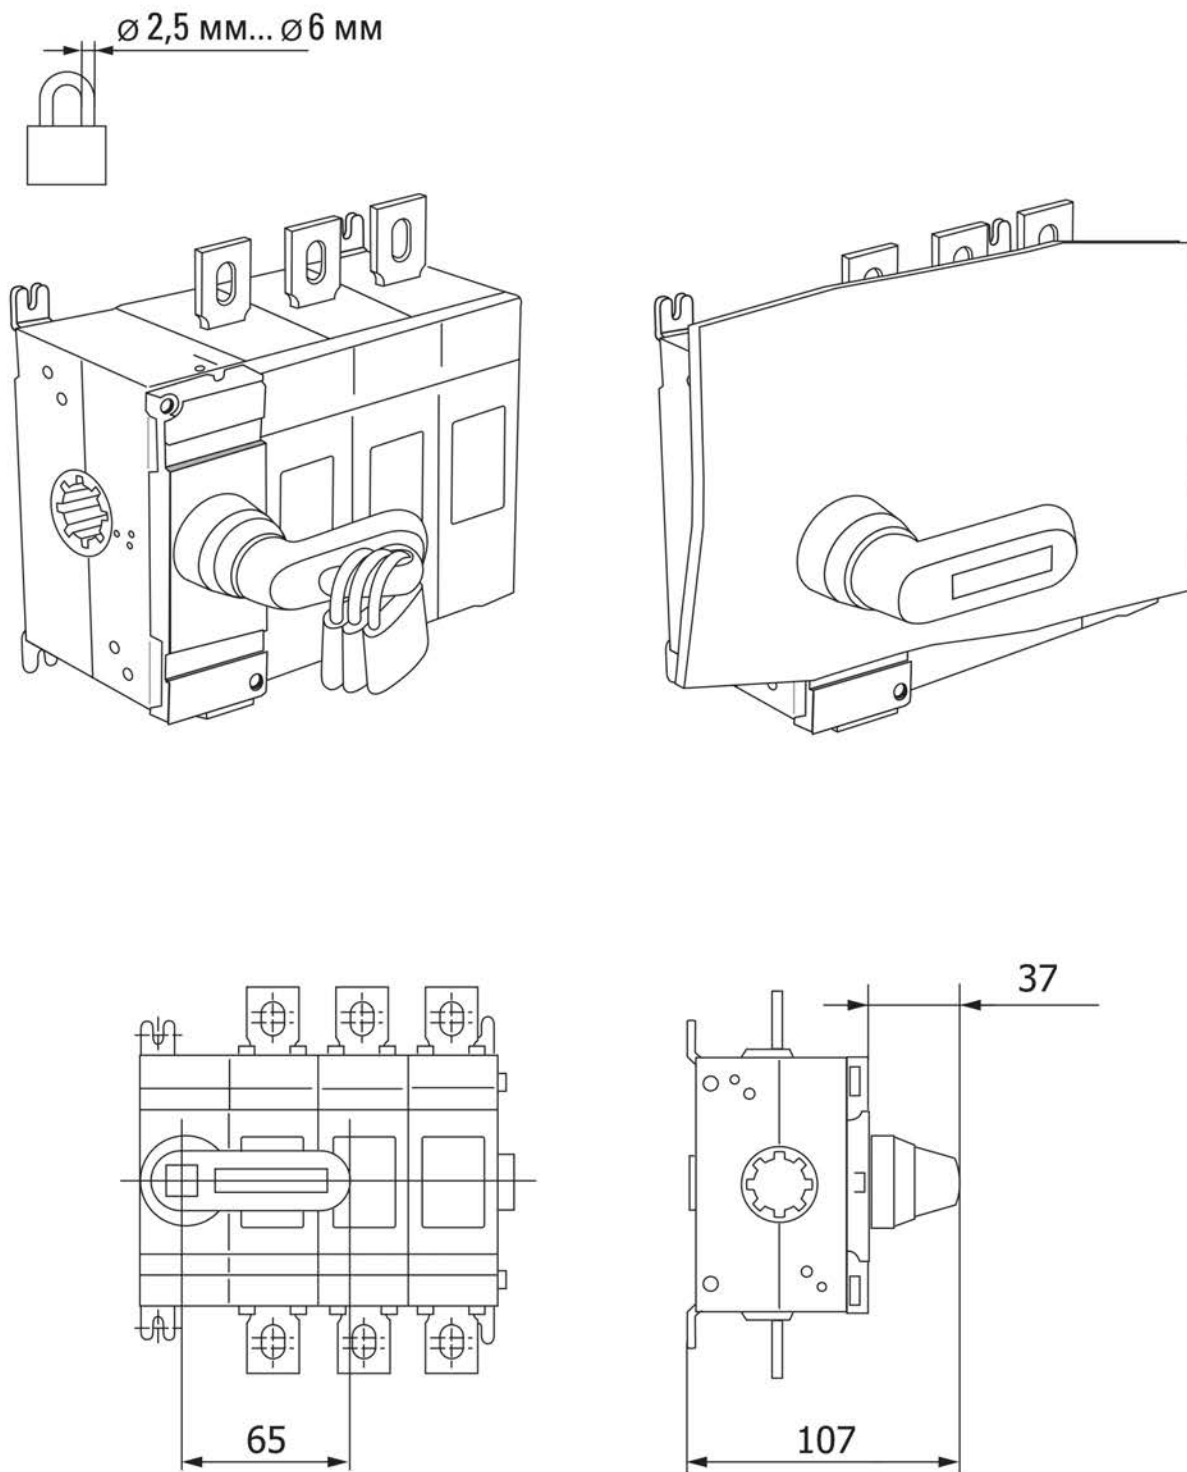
Установка рукоятки управления прямой установки 160-250 А
